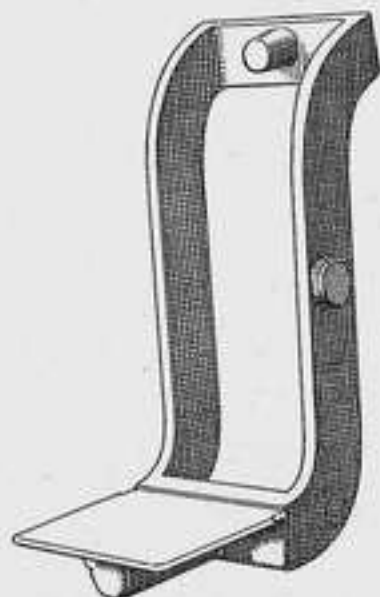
Lattenhalter mit aufgeschweißter Eisenplatte.
